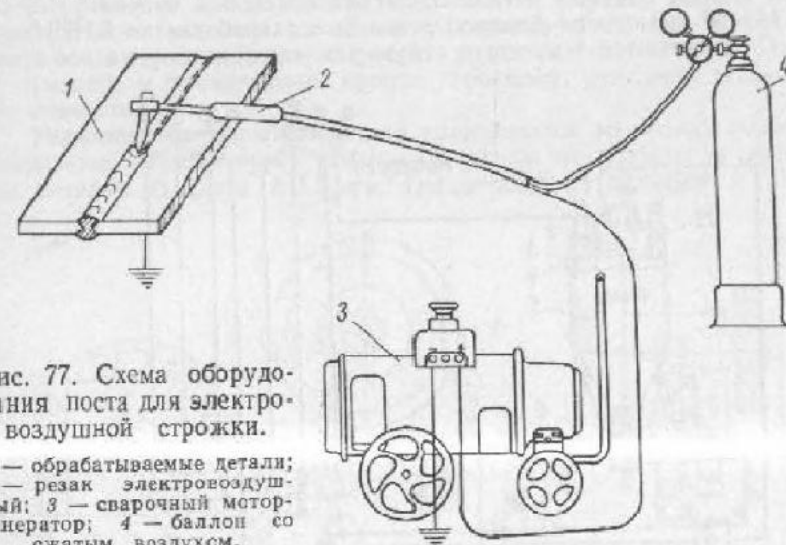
Схема оборудования поста для электровоздушной строжки.
